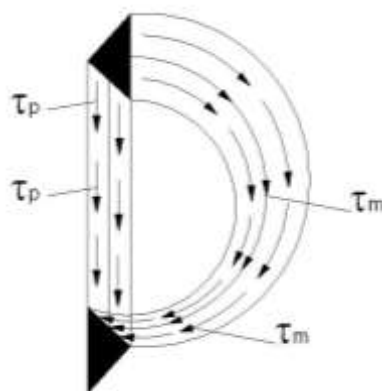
Diagrama cuerpo libre del cordón de soldadura
